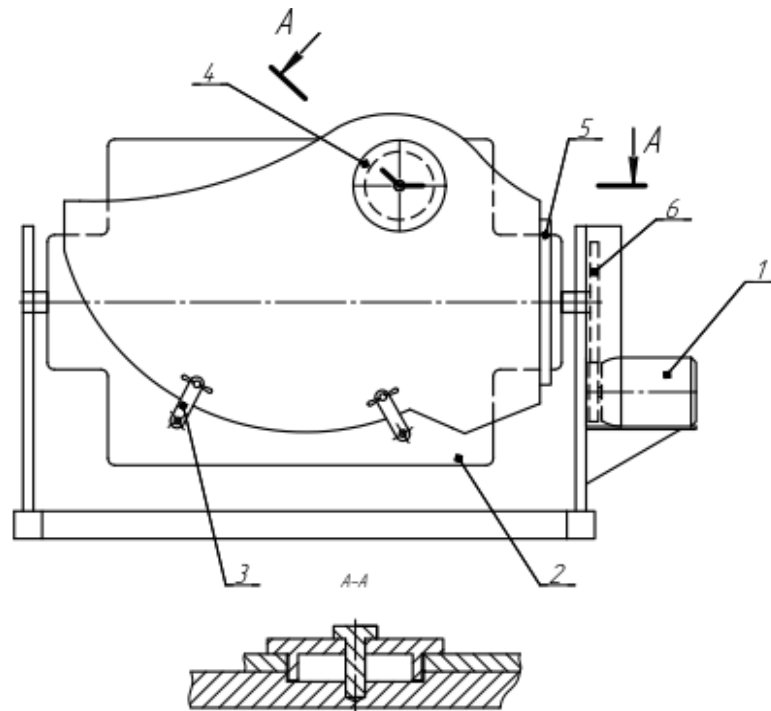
Складально-зварювальний стенд верстата: 1 – електродвигун; 2 – рама кондуктора; 3 – поворотні механічні затискачі; 4 – втулковий фіксатор; 5 - завзята планка; 6 – механізм обертання стенду
